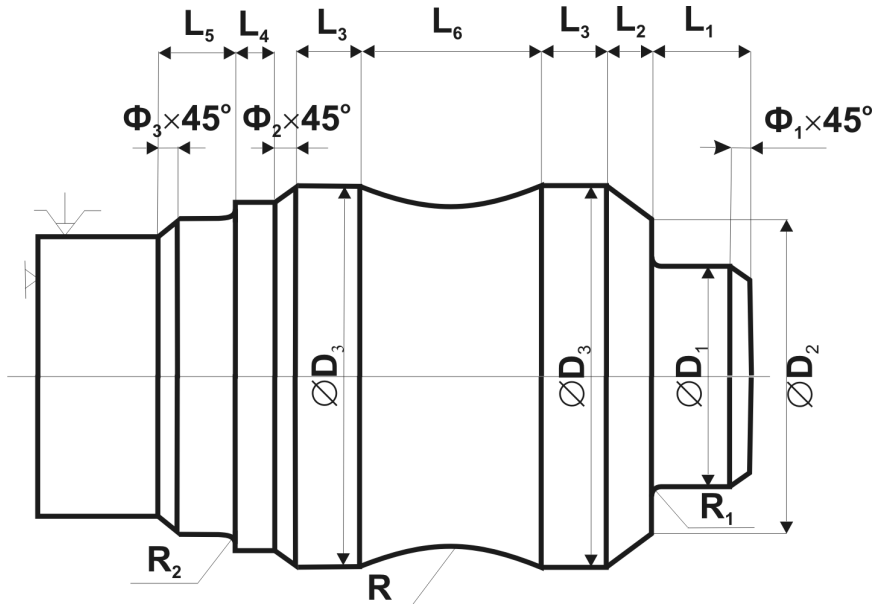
Ескіз деталі до лабораторної роботи 3
